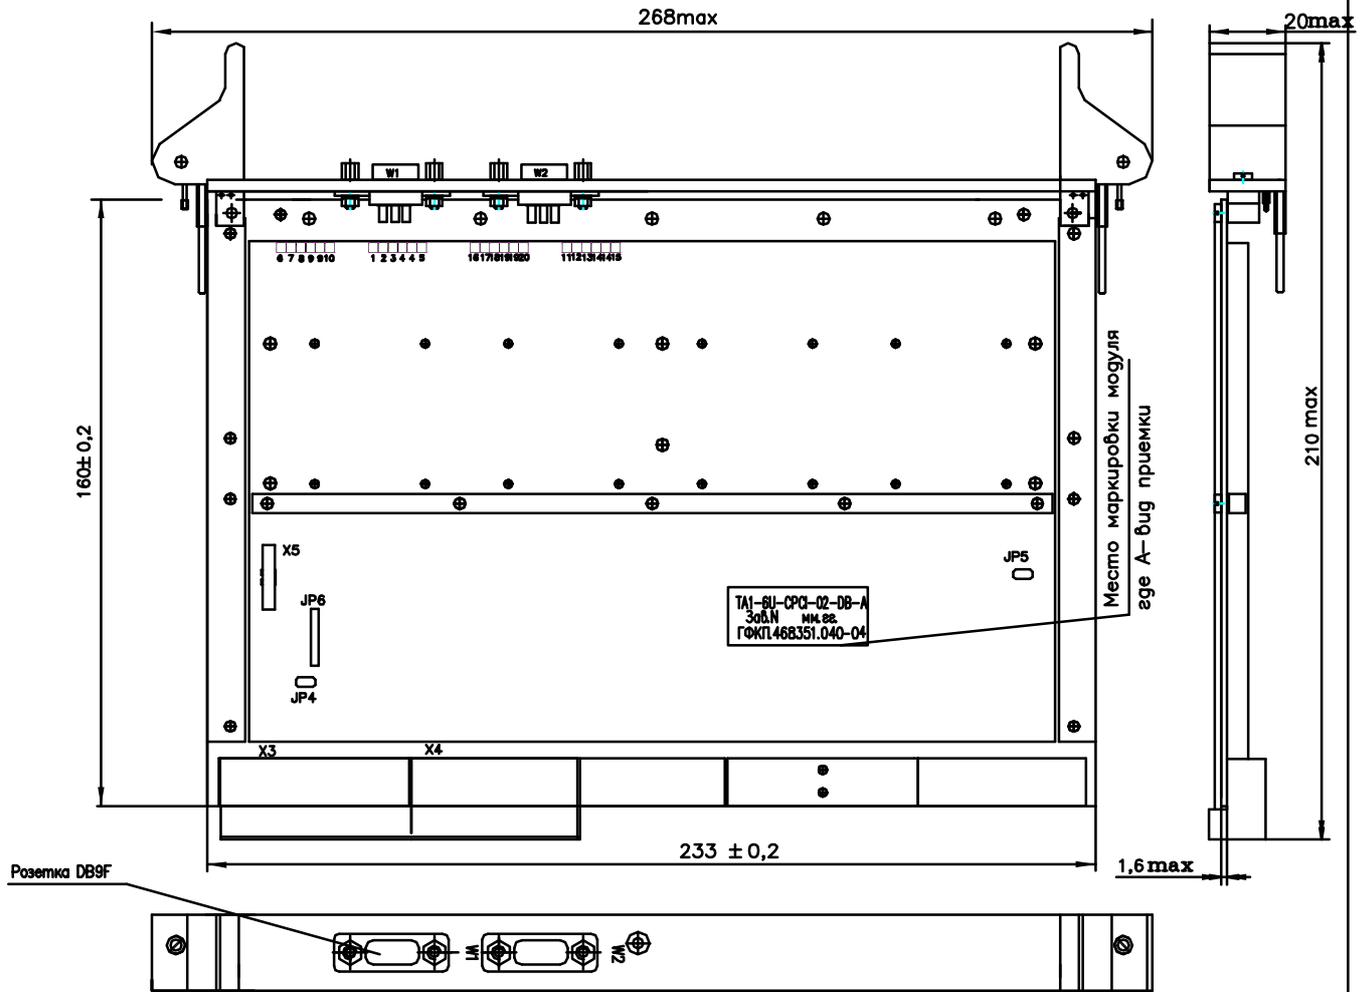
Габаритный чертеж изделия ТА1-6U-CPCL-02-DB –А без кондуктивного теплосъема с разъемами DB9
